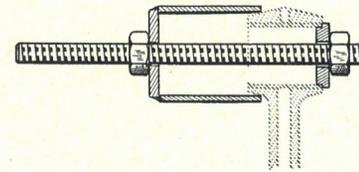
EXTRACTEUR MR-3682-120 POUR AXE DE PISTON
